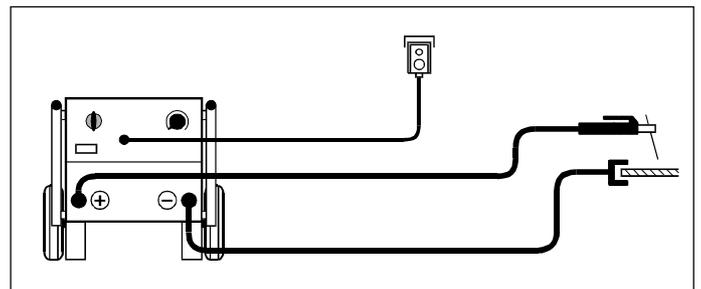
WTU als Stromquelle für E-HANDSCHWEISSUNG
